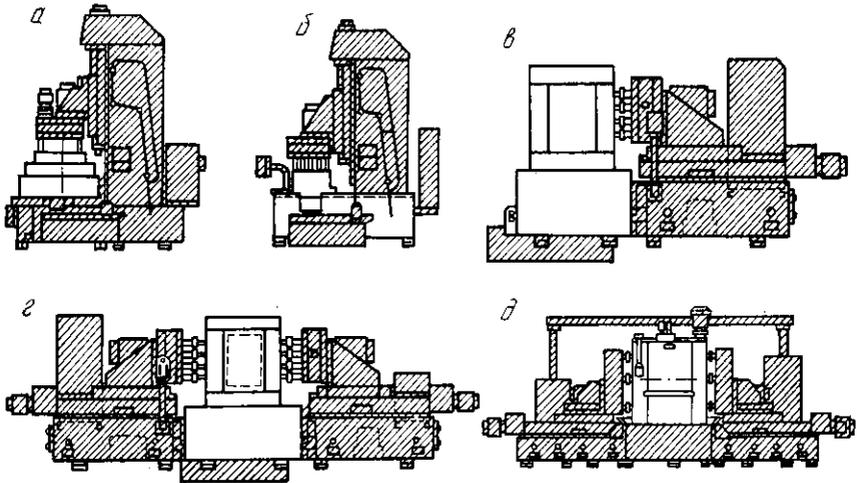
Унифицированные компоновки агрегатных станков:
